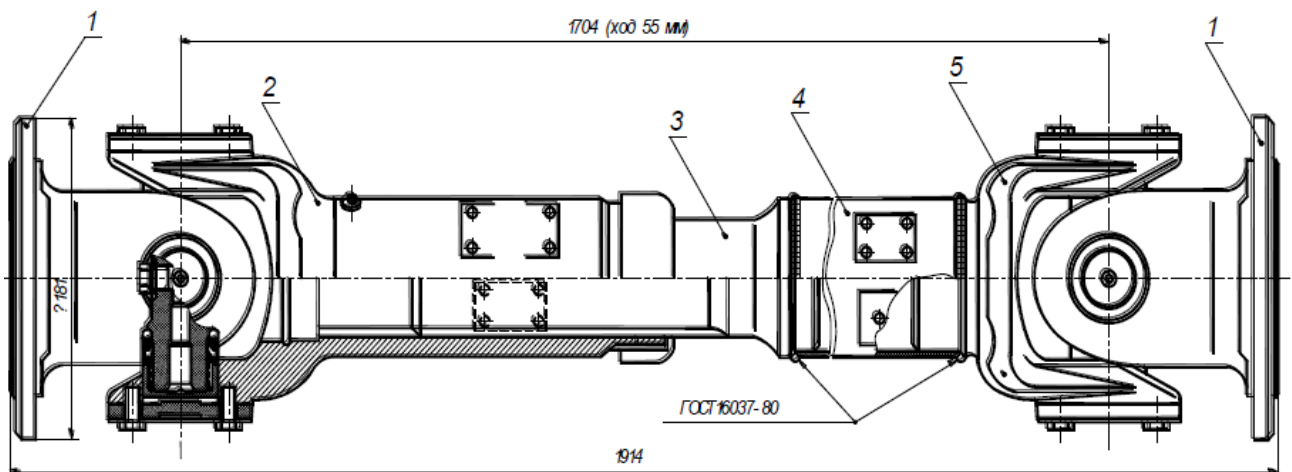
Кардан автомобіля КрАЗ-Н12.2: 1 – вилка із наконечником для кріплення фланця; 2 – вилка із другої сторони шліци; 3 – карданний вал із шліцем з іншої сторони; 4 – вал; 5 – вилка із наконечником для кріплення із валом.
